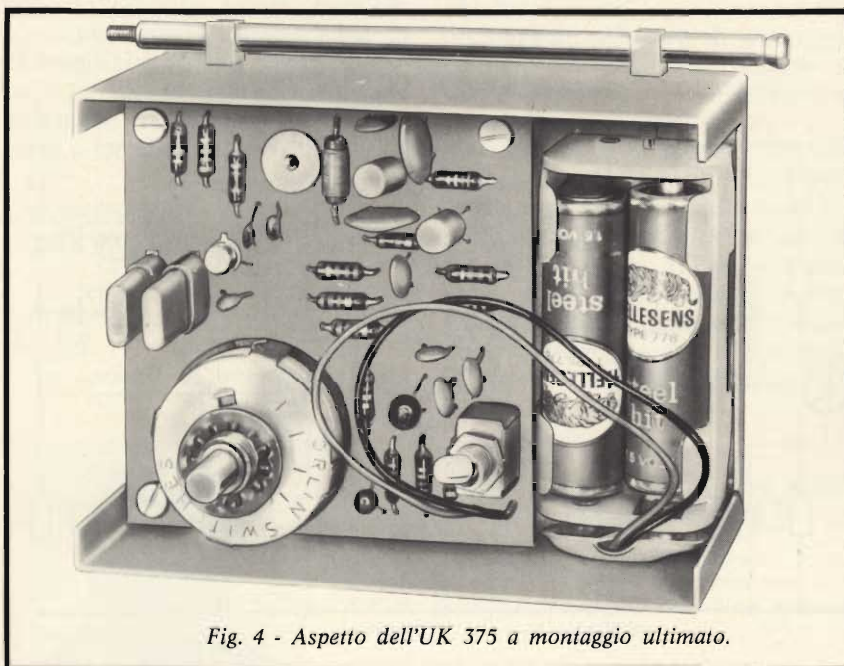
Aspetto dell'UK 375 a montaggio ultimato.
